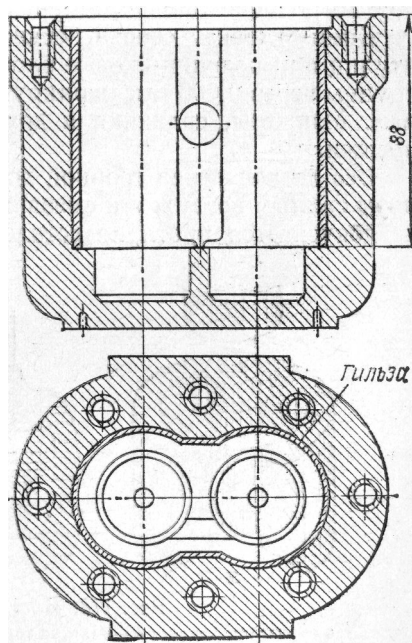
Гильза из алюминиевого сплава и корпус гидронасоса после гильзовки и расточки.
